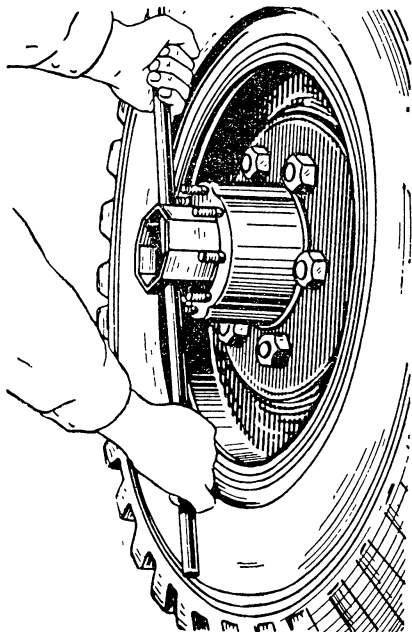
Регулировка подшипников ступицы колеса (затяжка регулировочной гайки у автомобилей ГАЗ-63, ГАЗ-69 и ГАЗ-69А)
